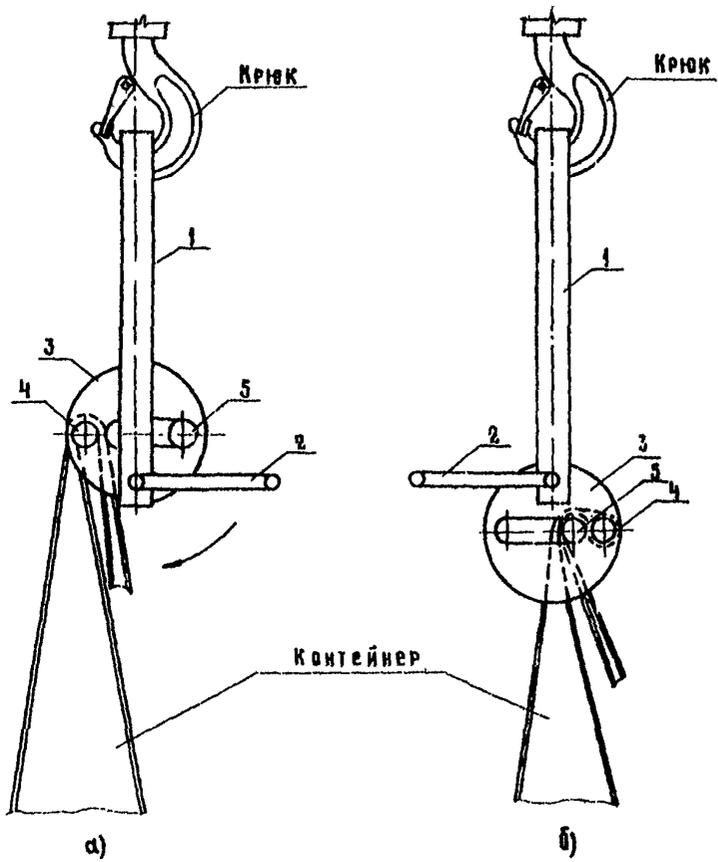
Парток строповки контейнера грузозахватным приспособлением с полумеханической запасовкой горловины: 1 - бугаль; 2 - рукоятка; 3 - диск; 4 - горизонтальная штанга; 5 - вертикальная штанга
